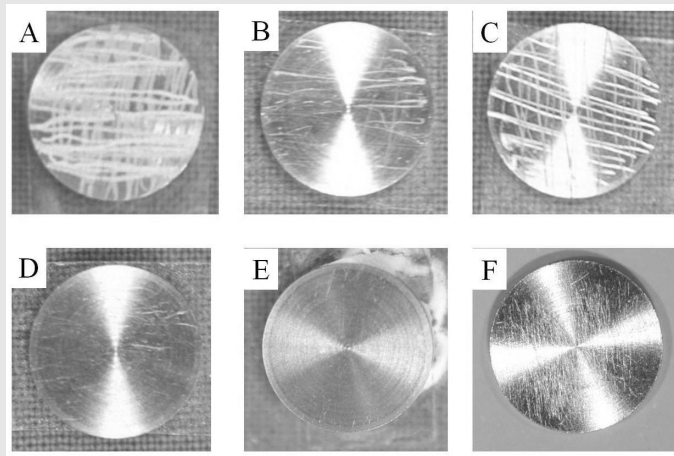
기구조작 후 육안으로 관찰 한 machined 티타늄 표면
